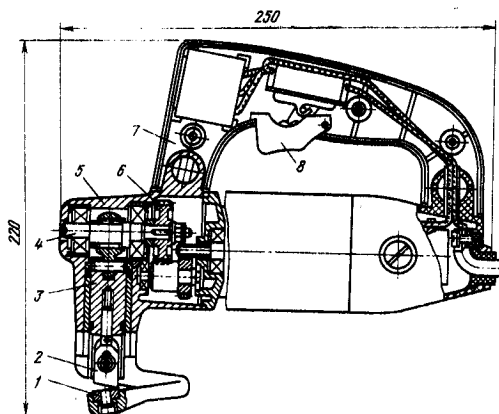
Ножницы ИЭ-5404: 1 — неподвижный нож; 2 — подвижный нож; 3 — ползун; 4 — эксцентрик; 5 — корпус; 6 — редуктор; 7 — рукоятка; 8 — курок
